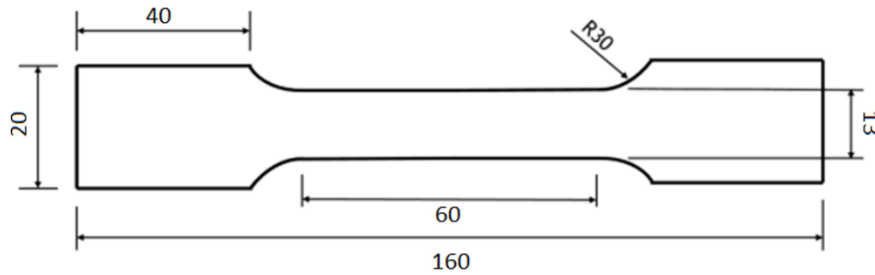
Exemplo das dimensões dos provetes em [mm] para ensaio de tração em solda [31].
